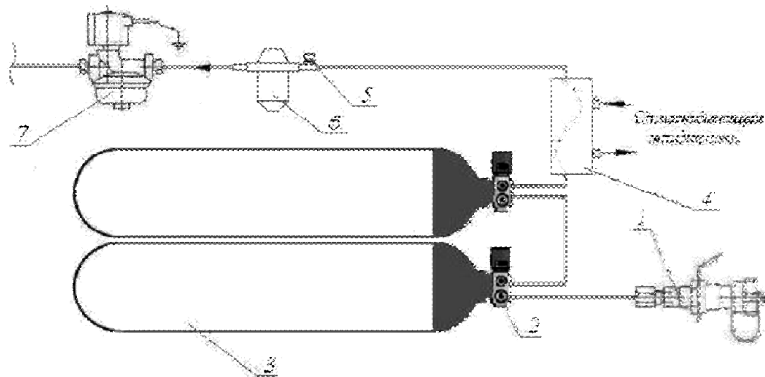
Схема подключения газобаллонной аппаратуры высокого давления: 1 – наполнительный вентиль; 2 – расходный вентиль; 3 – газовый баллон; 4 – подогреватель газа; 5 – сигналатор аварийной выработки газа; 6 – редуктор высокого давления; 7 – электромагнитный клапан с фильтром.
